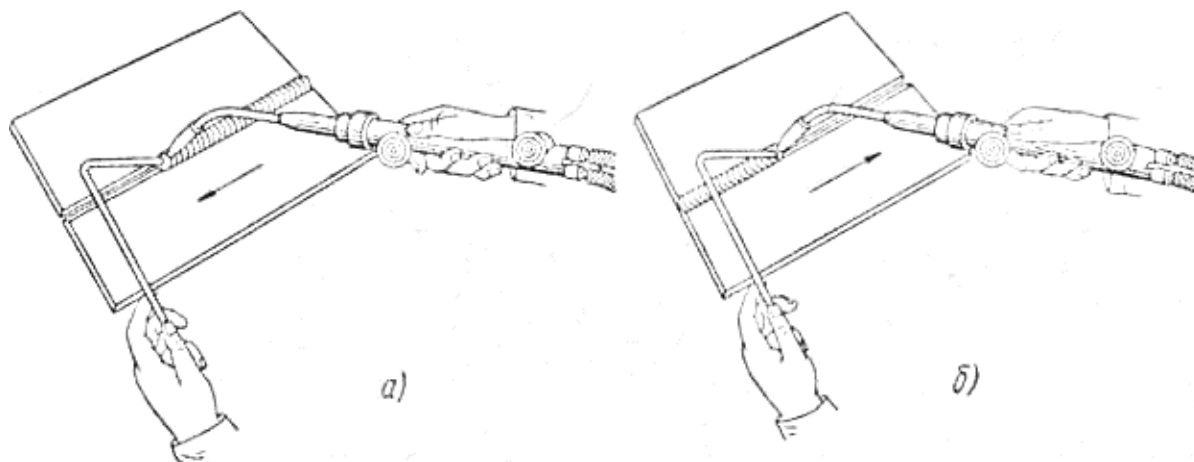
Способи виконання газового зварювання: а) лівий; б) правий
